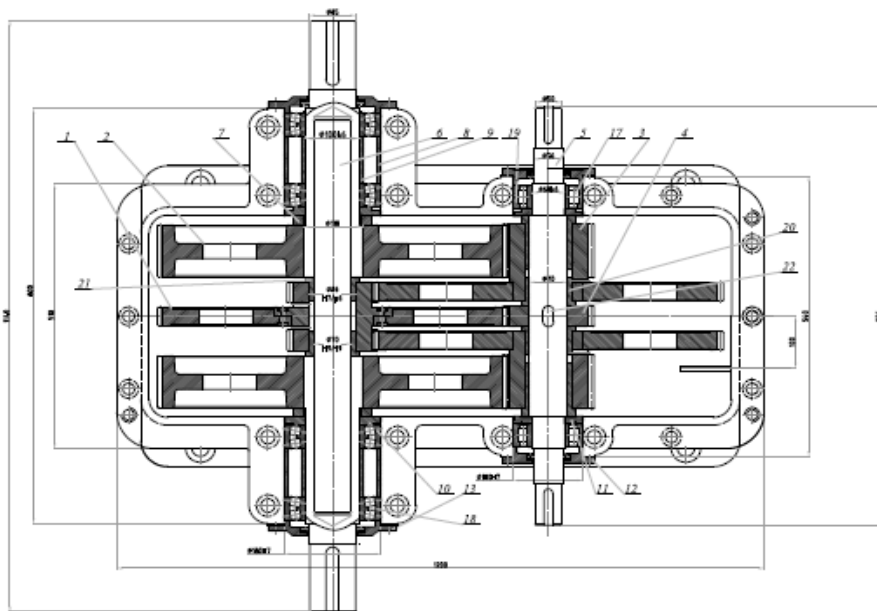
Двухпоточный трехступенчатый пакетный редуктор для станков-качалок
